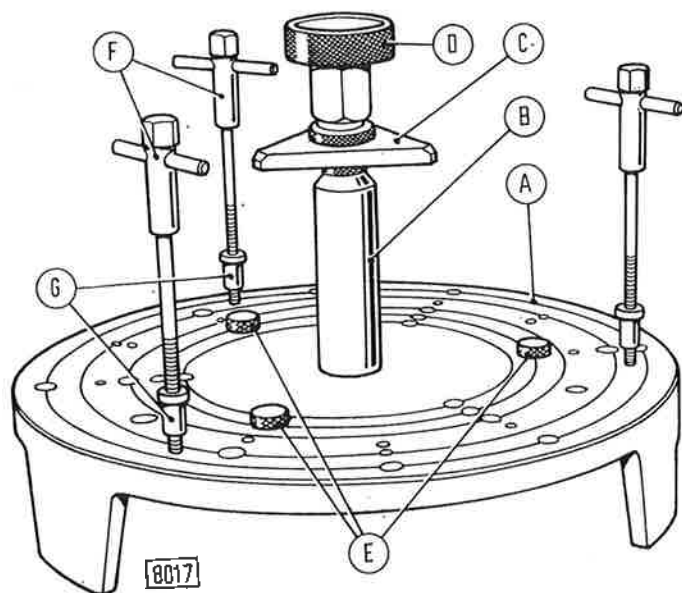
Pièces de la trousse universelle 291291/1 nécessaires pour réviser l'embrayage FERODO 12"/12".
